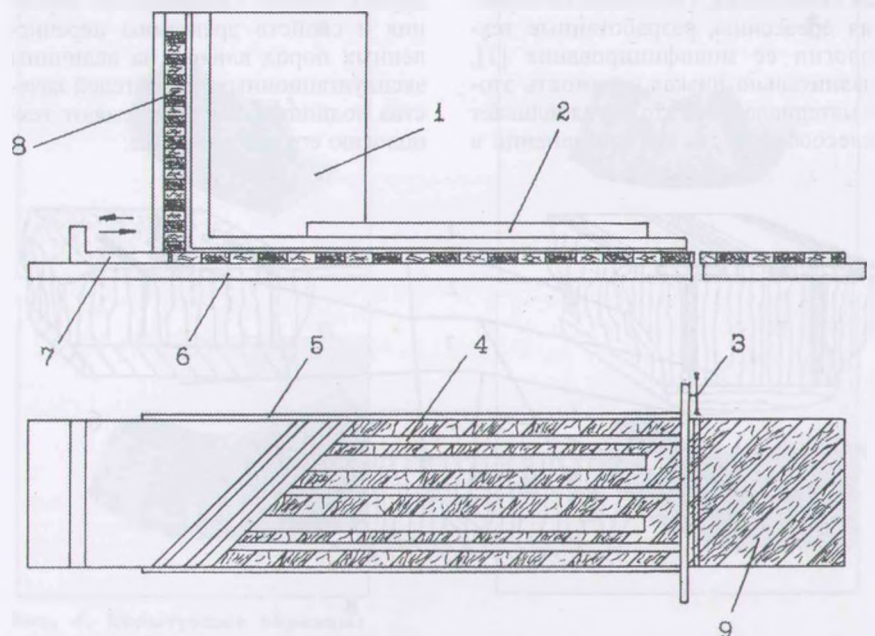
Схема станка для изготовления слоёв паркетного щита:
